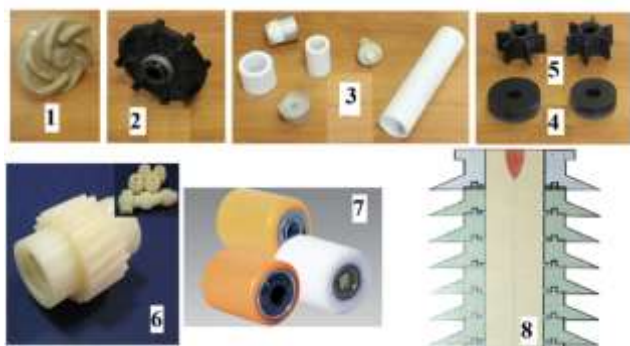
Изделия из СВМПЭ-композитов, полученные твердофазной объемной штамповкой: 1 – рабочее колесо центробежного насоса; 2 – рабочее колесо привода снегохода «Рысь»; 3 – детали механоактиватора моторного топлива; 4 – заготовки для штамповки рабочего колеса жидкостнокольцевого вакуумнасоса; 5 – рабочие колеса жидкостнокольцевого вакуумнасоса; 6 – зубчатое колесо; 7 – металло-полимерные подшипники скольжения; 8 – опорный изолятор в сборе.
